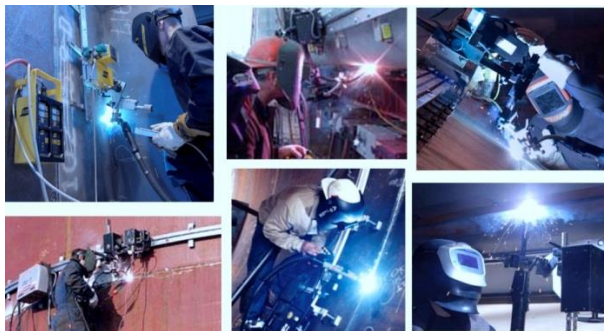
Operadores de manipuladores tendo que acompanhar o dispositivo durante a soldagem [3,14].
